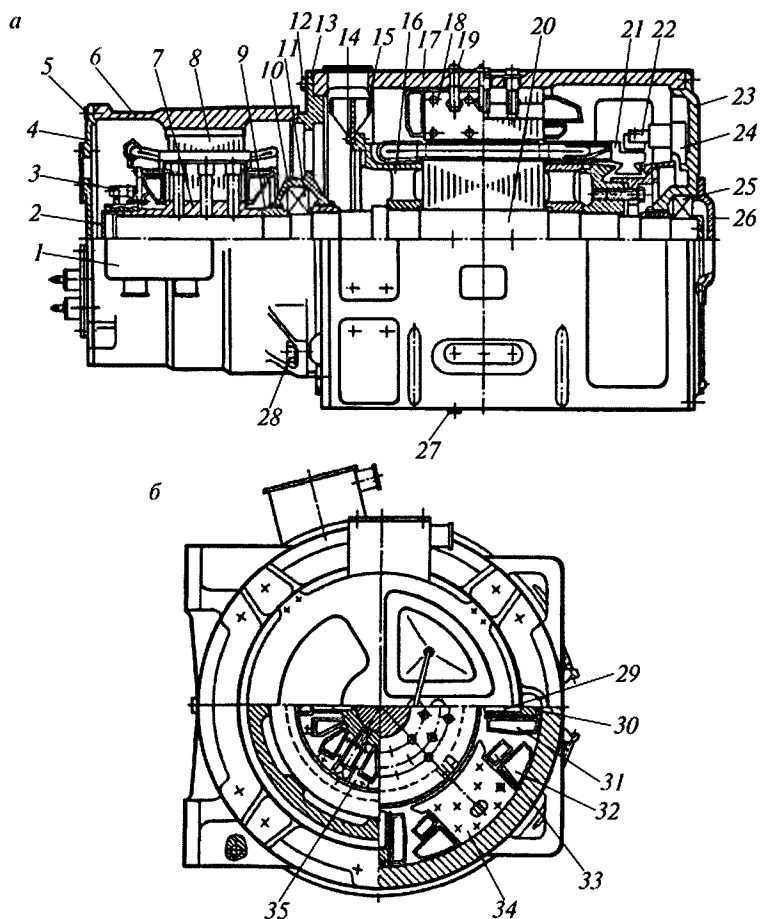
Продольный (а) и поперечный (б) разрезы преобразователя 1ПВ-6У1: 1 — коробка выводов; 2 — шайба; 3 — пальцы щеткодержателя; 4 — подшипниковый щит генератора; 5, 12, 14, 28 — болты; 6 — станина генератора; 7, 9 — втулки; 8 — сердечник статора; 10, 26 — крышки подшипника; 11, 25 — роликовые подшипники; 13, 23 — подшипниковые щиты; 15 — вентилятор; 16 — обмоткодержатель; 17 — остов двигателя; 18 — обмотка якоря; 19 — бронзовый болт; 20 — вал; 21 — коллектор двигателя; 22 — щеткодержатель; 24 — траверса; 27 — пробка для слива конденсата; 29 — сердечник добавочного полюса; 30 — латунные прокладки; 31 — катушка добавочного полюса; 32 — катушка независимого возбуждения; 33 — катушка последовательного возбуждения; 34 — сердечник главного полюса; 35 — полюса ротора генератора
